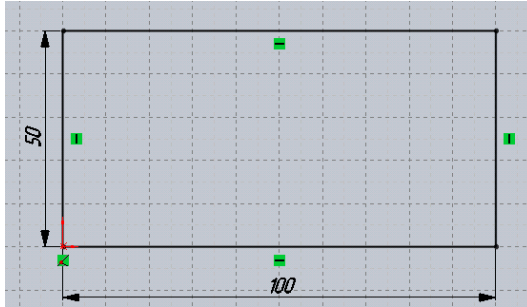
Ескіз моделі стикового зварного з'єднання
